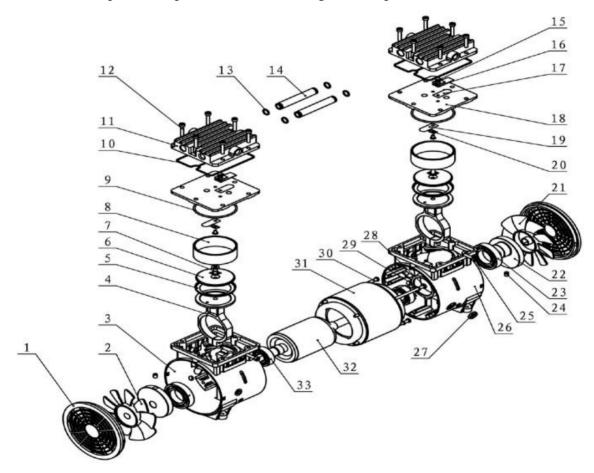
Explosionado de compresor de pistón sin aceite.
